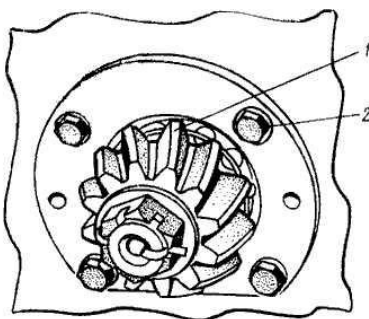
Снятие ведущей шестерни главной передачи: 1 — ведущая шестерня; 2 — болт
